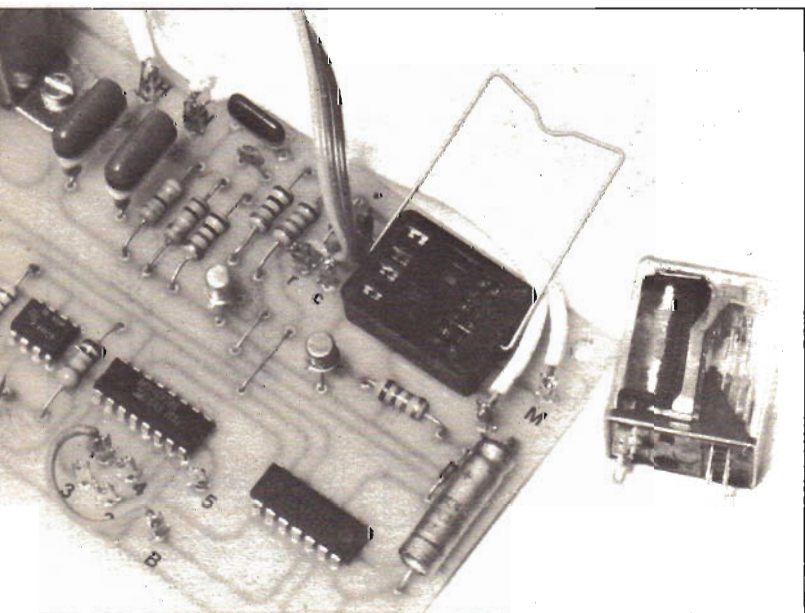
Lo zoccolo del relè può avere una staffa di fissaggio.
